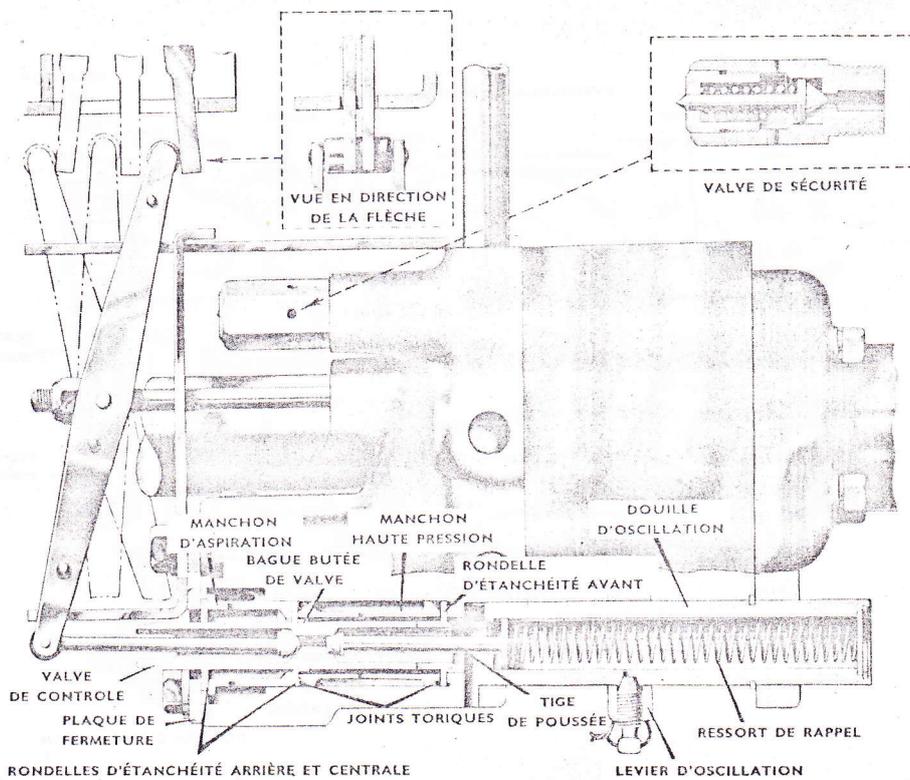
COUPE DU DISPOSITIF D'ENSEMBLE DE LA VALVE DE CONTRÔLE.
